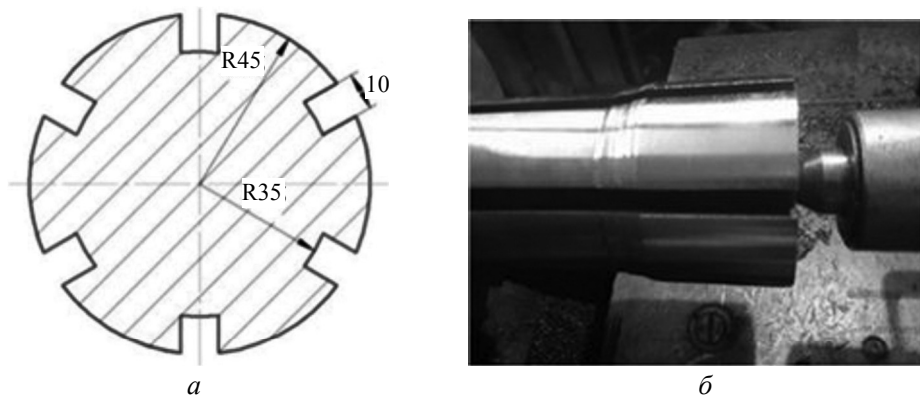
Поперечний переріз (а) заготовки та її установка на верстаті (б).
